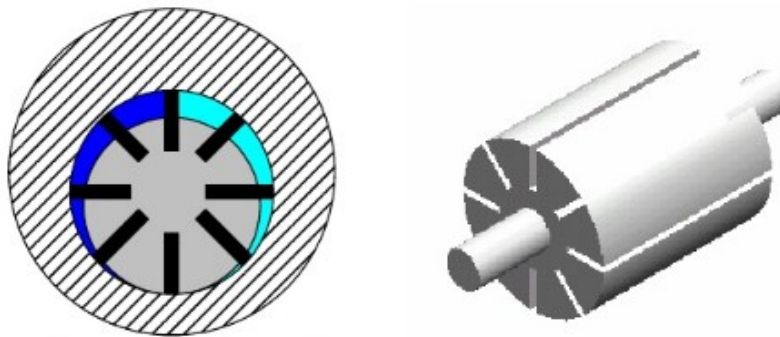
Detalle del funcionamiento y rotor del motor de paletas.
